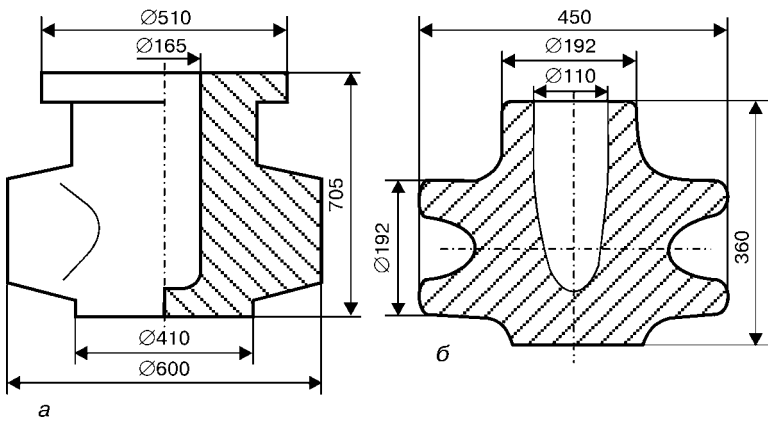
Схемы заготовок ЭШЛ: а – корпуса энергетической задвижки; б – тройника
